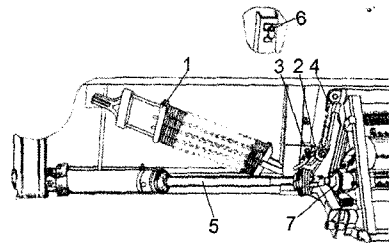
Уравнивающий механизм жатки (левый):
